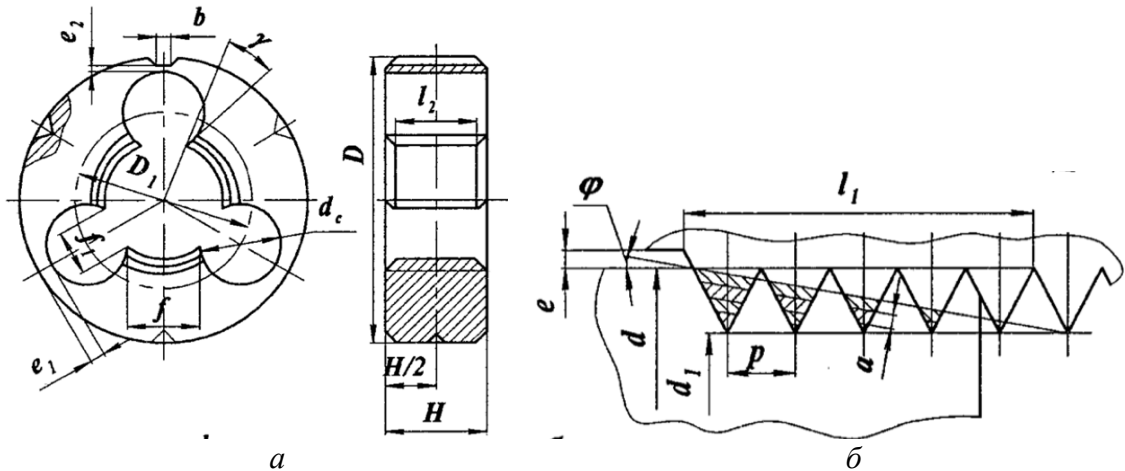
Конструкція різьбонарізної плашки: *а* - загальний вигляд; *б* - елементи різальної частини
